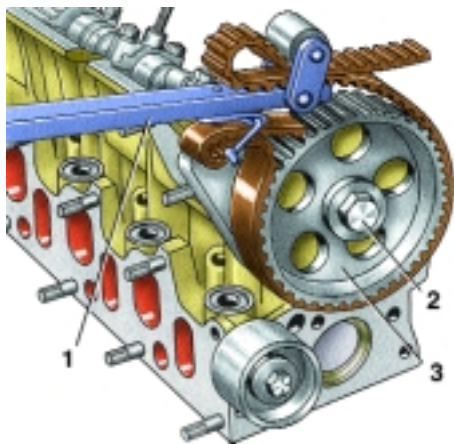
Крепление зубчатого шкива распределительного вала двигателя F3R 272: 1 – приспособление для удержания шкива; 2 – болт крепления шкива; 3 – шкив
